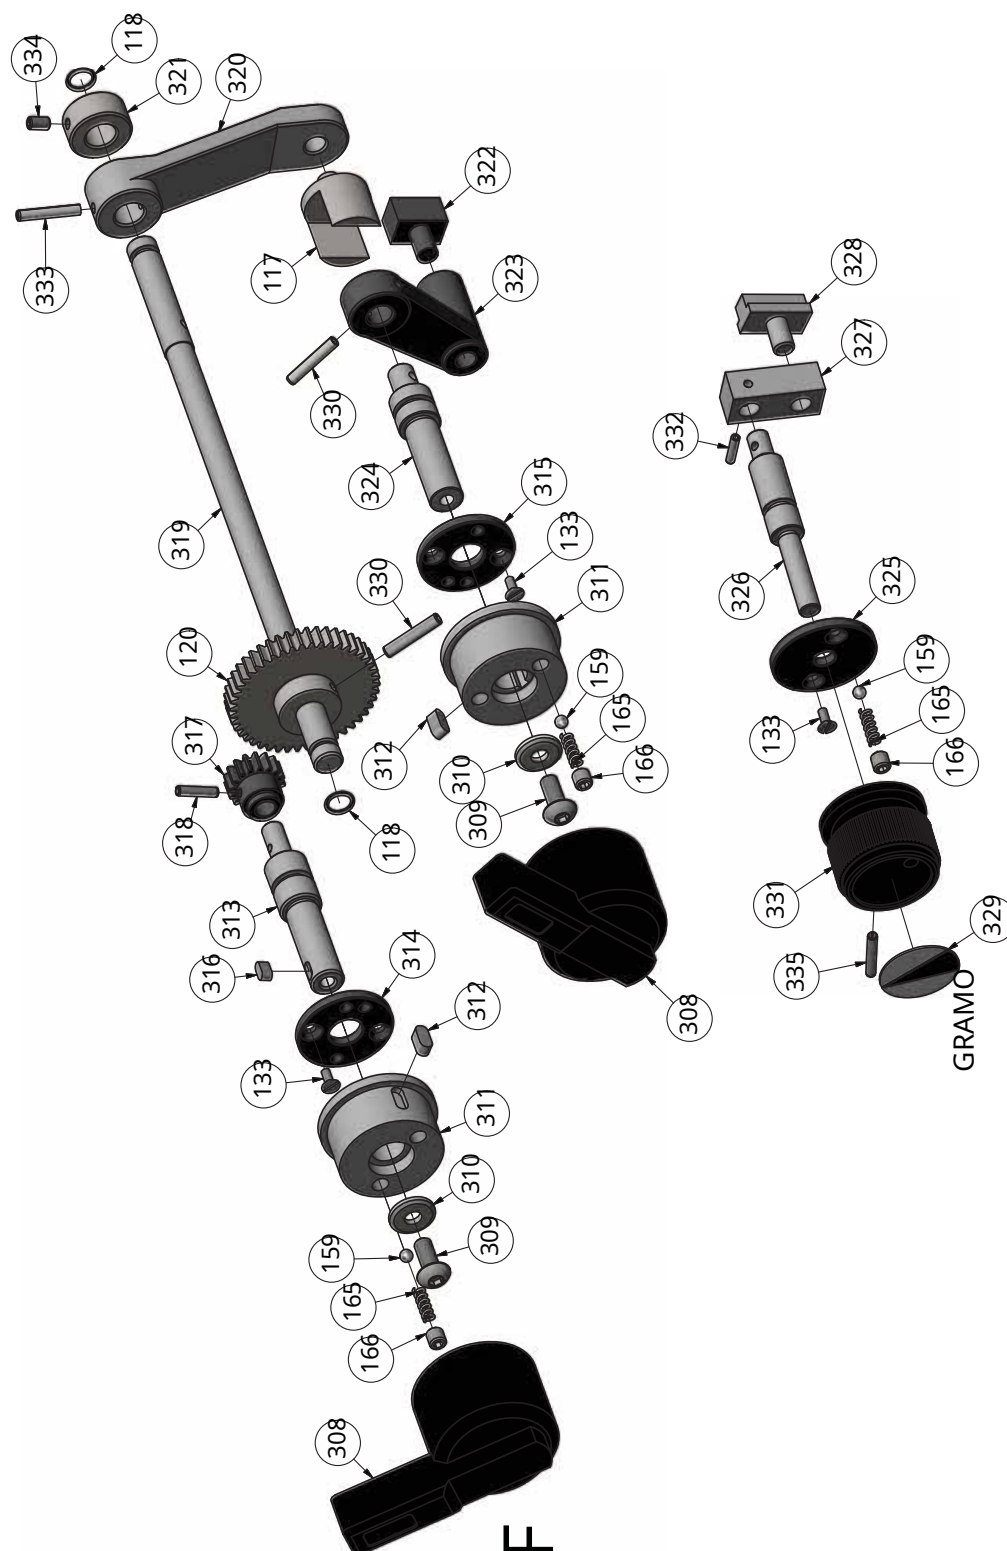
Getriebe Spindelstock 6-6 - Engranaje del cabezal 6-6
